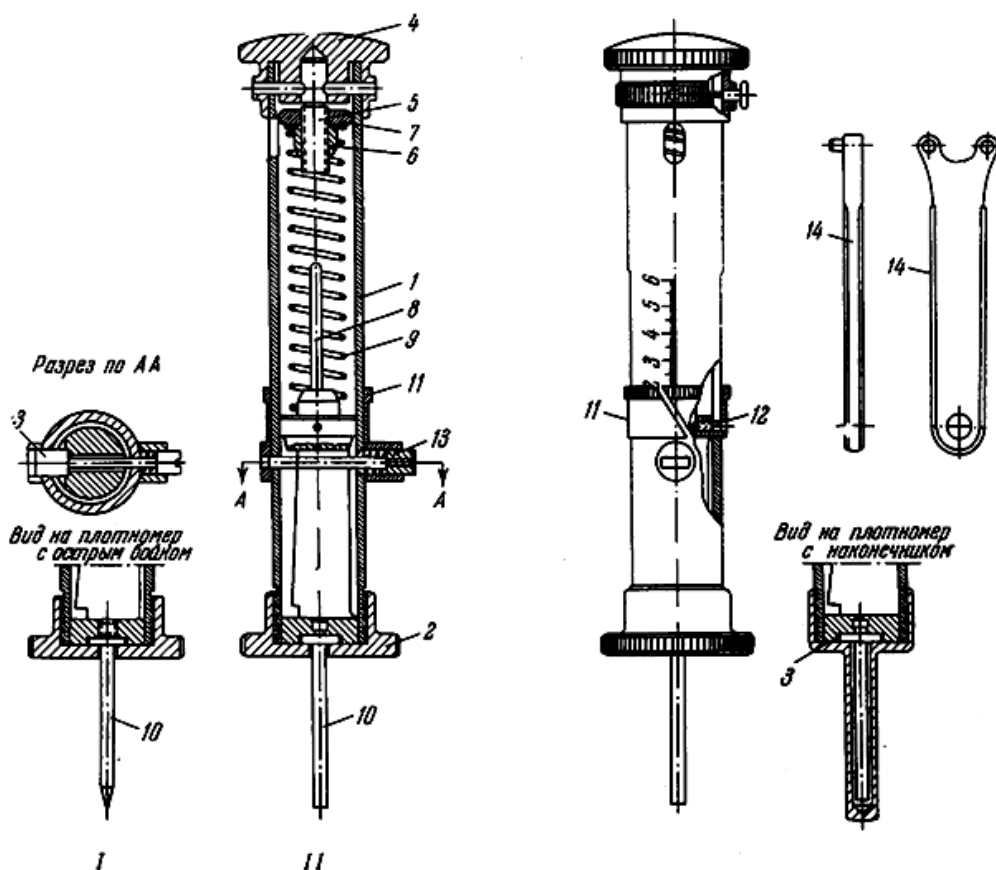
Твердомер Качинского (I – твердомер с острым бойком; II – твердомер с наконечником) 1 – металлический корпус; 2-опорный диск; 3-глухой наконечник; 4-головка; 5-винт; 6 и 7-шайбы; 8-поршень; 9-пружина; 10-плунжер; 11-кольцо-указатель; 12-винты; 13-кнопка; 14-ключ.
